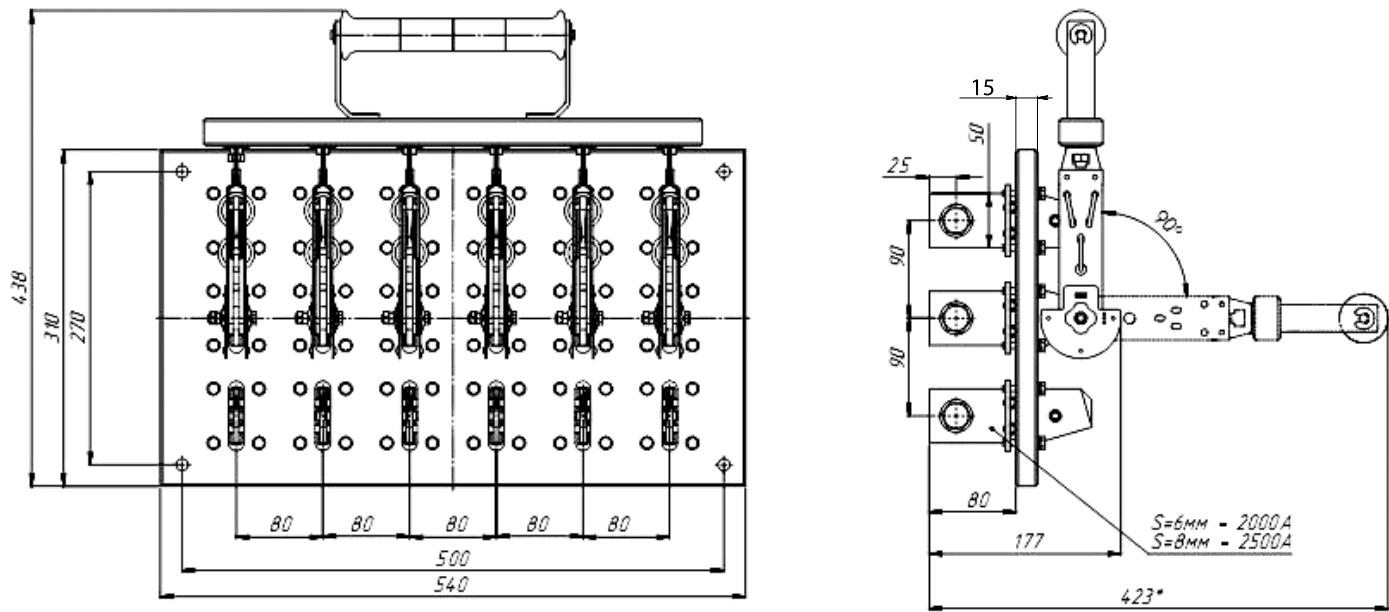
Разъединитель РЕ19 на два направления с центральной рукояткой
